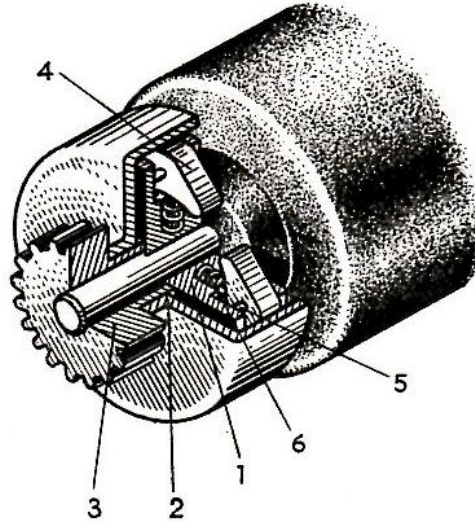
1 — катушка; 2 — чашечка; 3 — шестерня; 4 — грузики; 5 — ось грузика; 6 — пружина.
